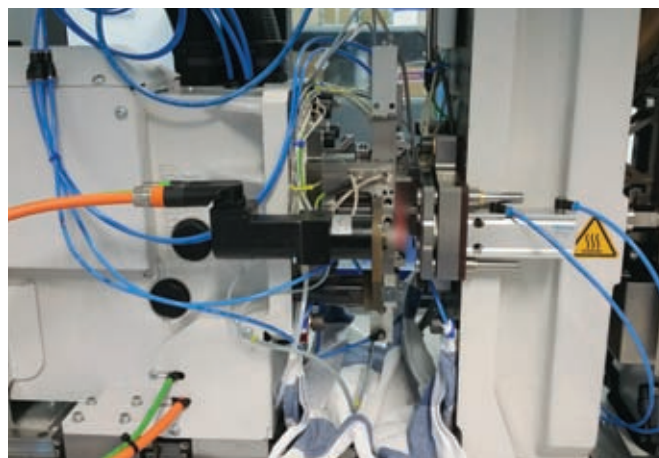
Литьевая форма со встроенной системой выкручивания резьбовых знаков (фото: mikrotechnik HIRT)
